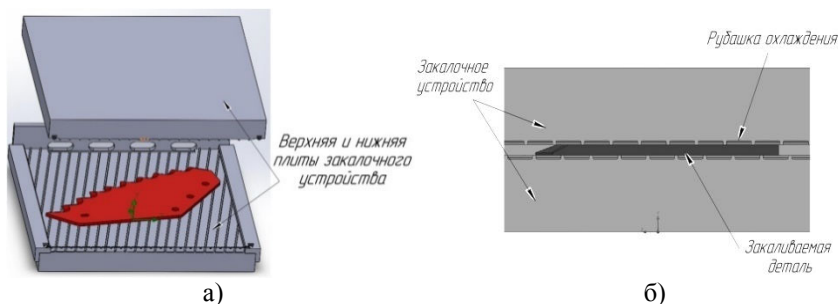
Расположение заготовки при загрузке в закалочное устройство (а) и закалочном охлаждении (б)
